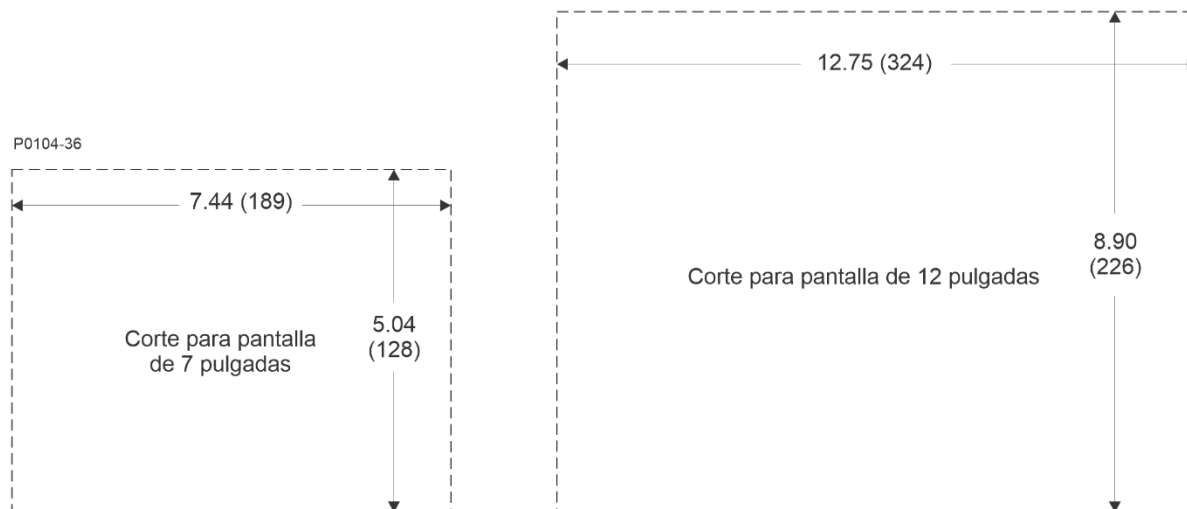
Dimensiones de corte del panel del IDP-2020
